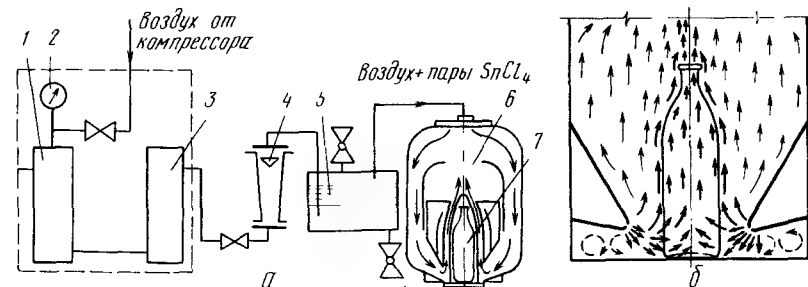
Схемы установки НОМ-3 для нанесения оксидно-металлических покрытий на стеклотару (а) и циркуляции паровоздушной смеси в рабочей камере (б)
